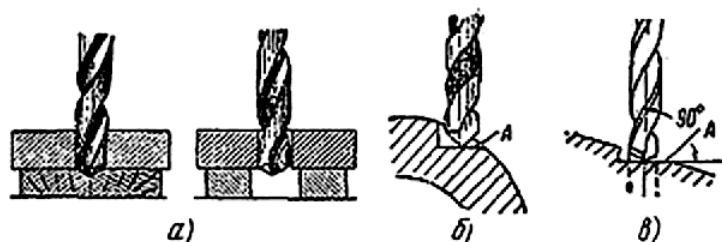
Сверление отверстий насквозь (а), на цилиндрической (б) и наклонной поверхностях (в)
